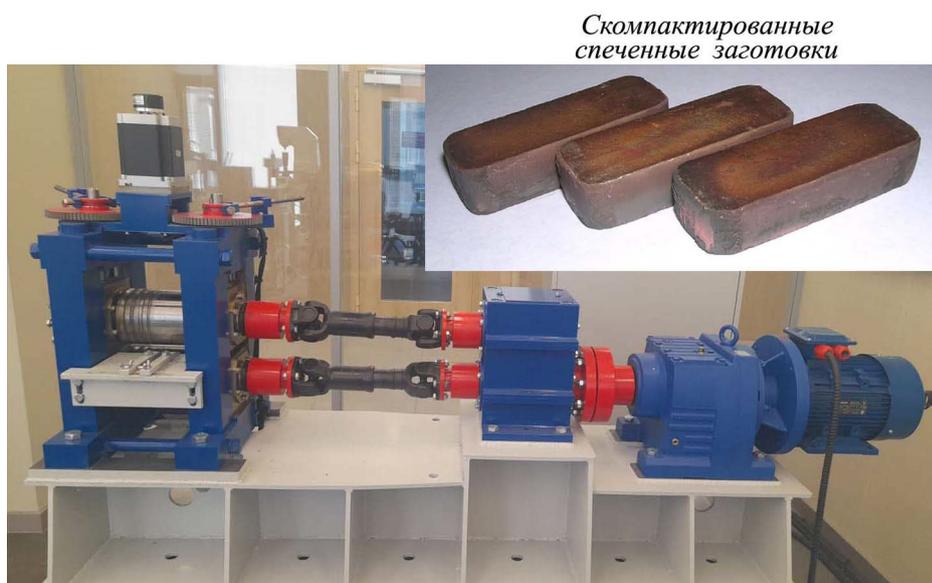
Лабораторный двухвалковый прокатный стан ДУО130
